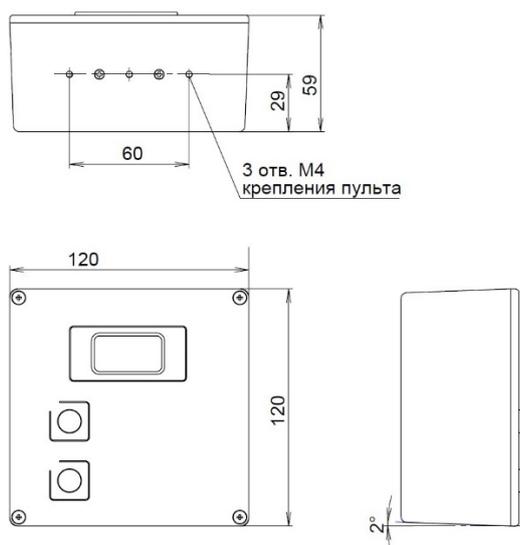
Габаритные размеры и присоединительные отверстия АРТО-PRO
